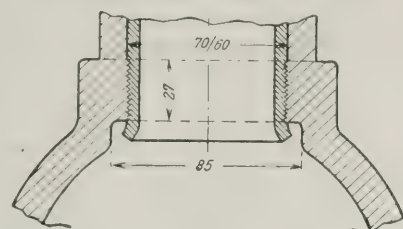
Befestigung der Wasserröhren im Grundring beim Brotan-Kessel.
